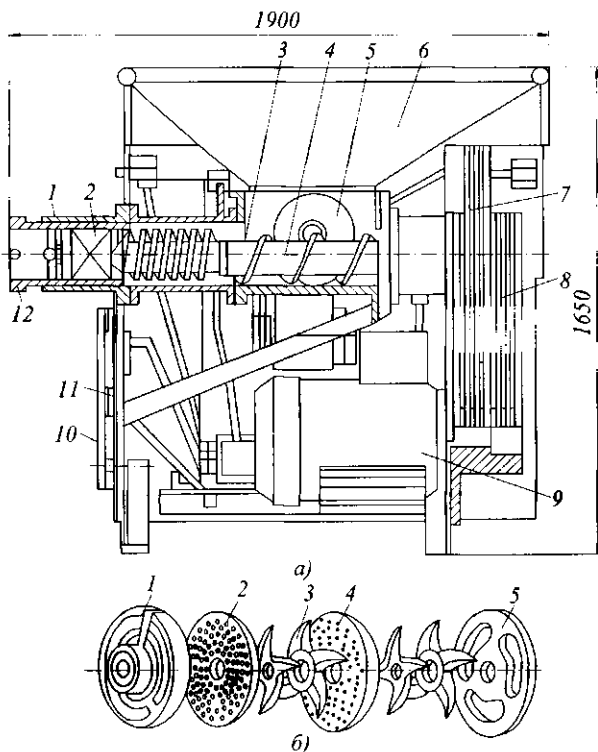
Волчок К7-ФВП-160-2: а – схема волчка; б – режущий механизм
